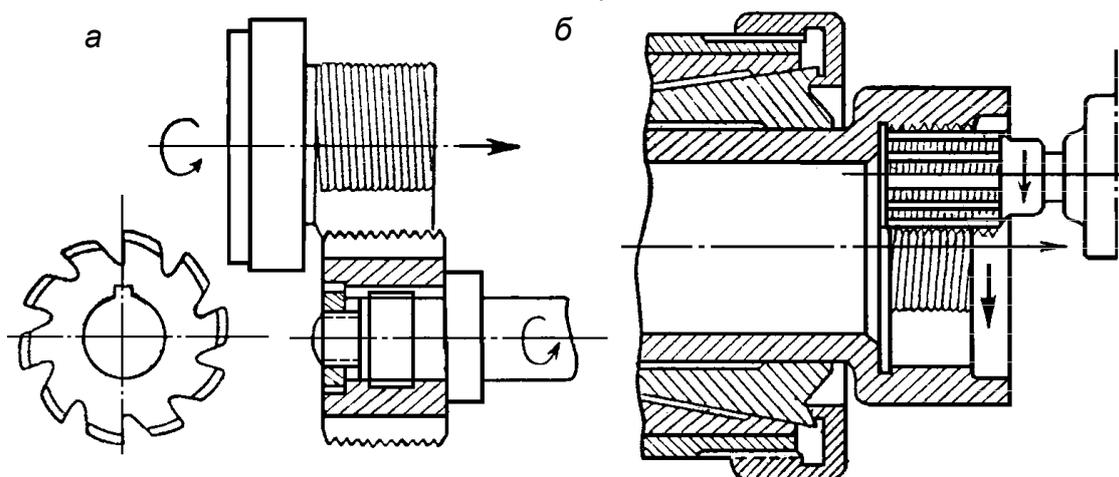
Схемы образования резьбы фрезерованием: а – наружной; б – внутренней нарезаемой резьбы
